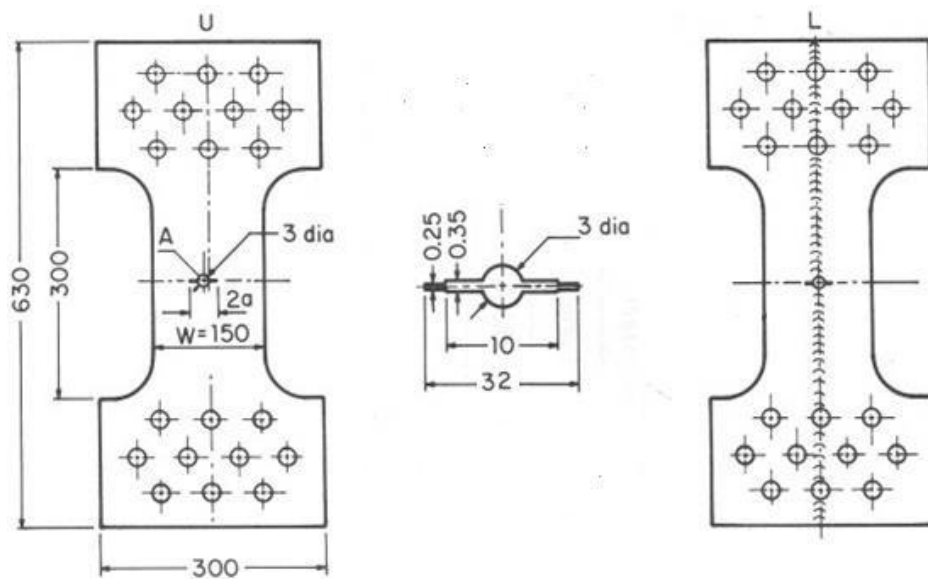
9: modèles géométriques des éprouvettes soudées et non soudées
